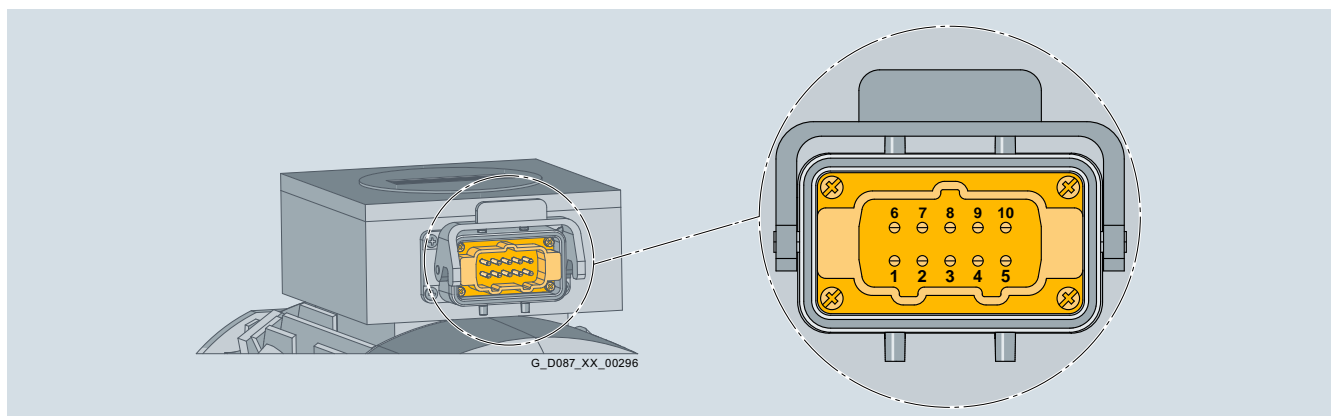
/18 Motorstecker HAN 10 E mit Pinbelegung
